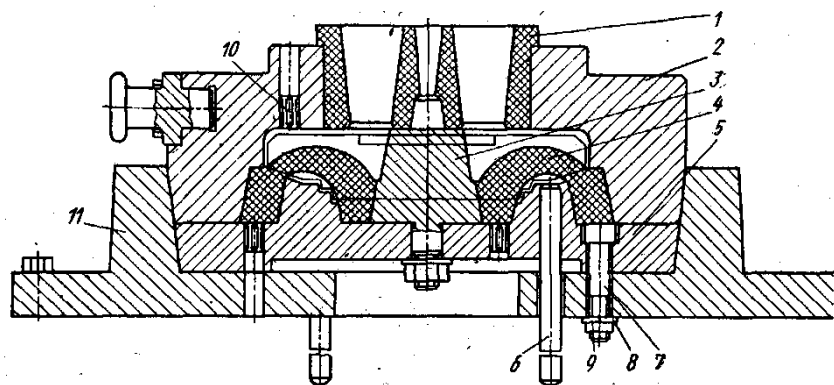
Кокиль для изготовления реактора гидротрансформатора ТР-325:
